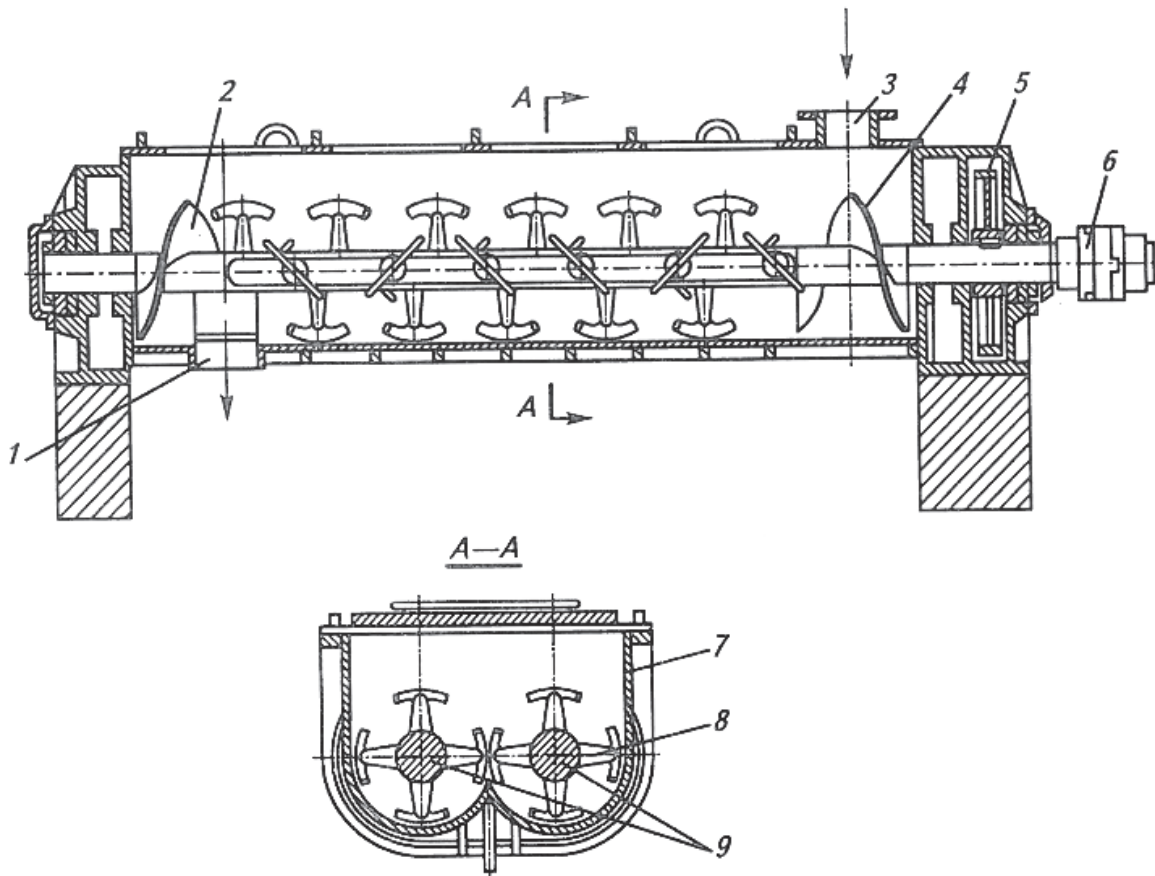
Смеситель с двумя шпорообразными роторами
